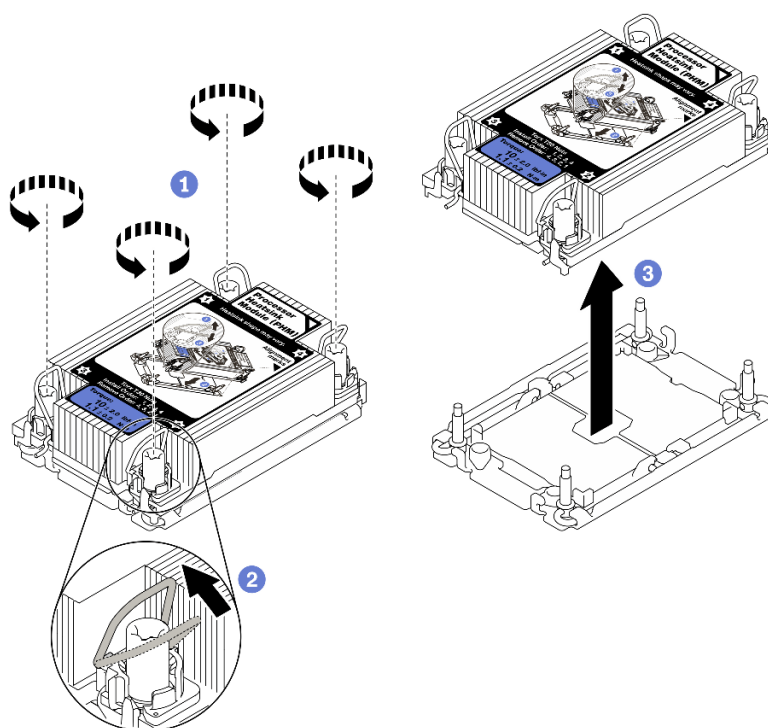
Retrait d'un module de processeur-dissipateur thermique
